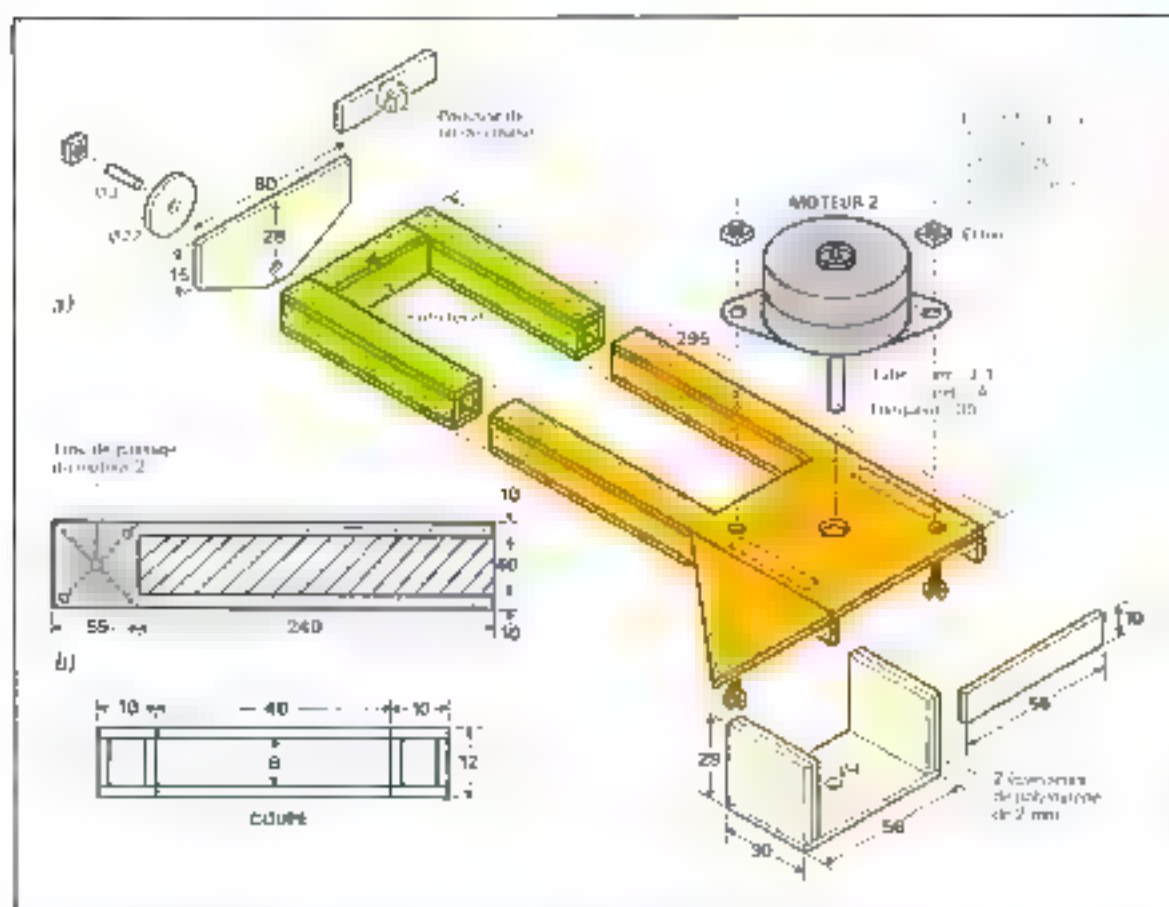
Dessin technique de la table traçante. a) Vue éclatée de l'ensemble. b) Coupe transversale et plan de la table traçante.
